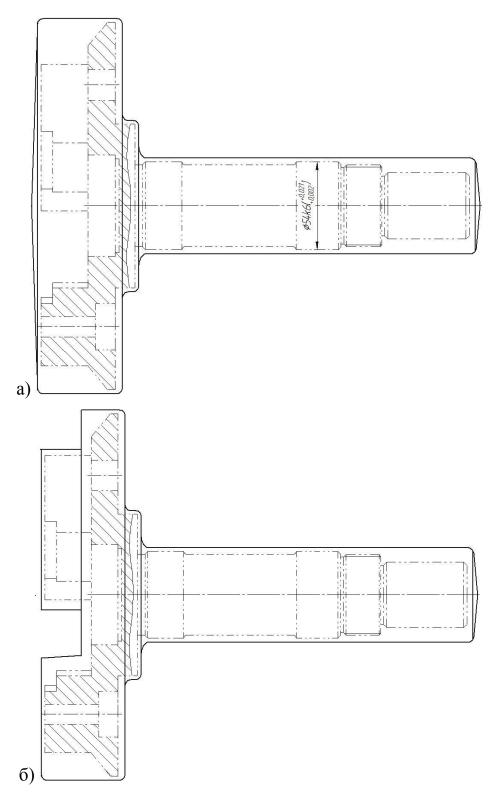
Эскизы заготовок: а) штамповка, б) отливка
